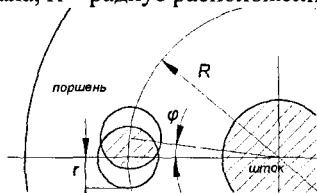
Перекрывание каналов при угловых перемещениях штока
